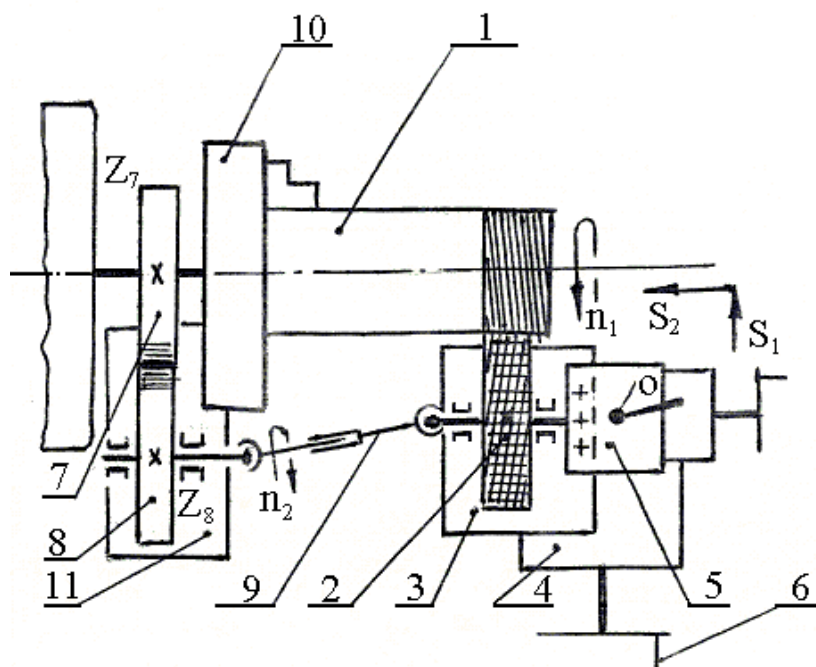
Схема фрезерования наружной резьбы (вид сверху): 1 – деталь с резьбовой поверхностью, 2 – червячная фреза, 3 – фрезерная головка, 4 – суппорт станка, 5 – резцедержатель, 6 – рукоятка поперечной подачи суппорта (резцедержателя), 7, 8 – гитара деления резьбы на заходы, 9 – карданный вал, 10 – патрон станка (для установки детали), 11 – кронштейн гитары деления.
